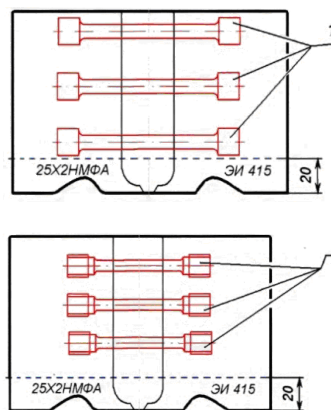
Схема вырезки образцов для испытания на растяжение металла контрольного сварного соединения сталей 25Х2НМФА+ЭИ415:
